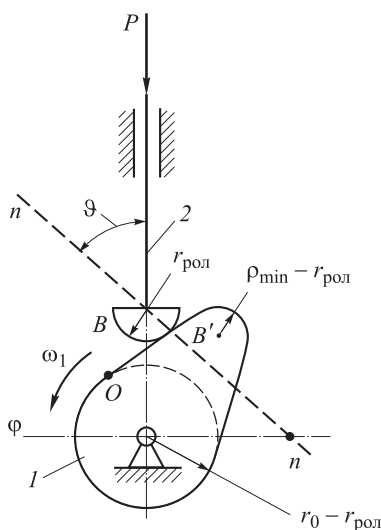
Кулачковый механизм с поступательным двигающимся толкателем:
